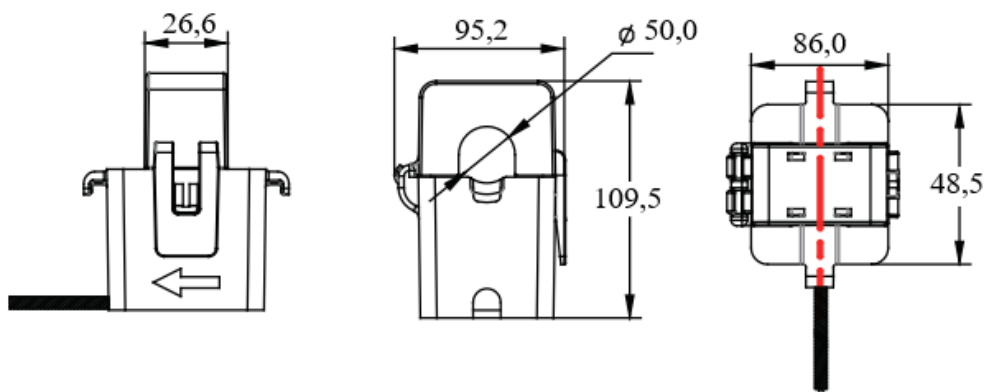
Внешний вид и габаритные размеры датчика SCT600
